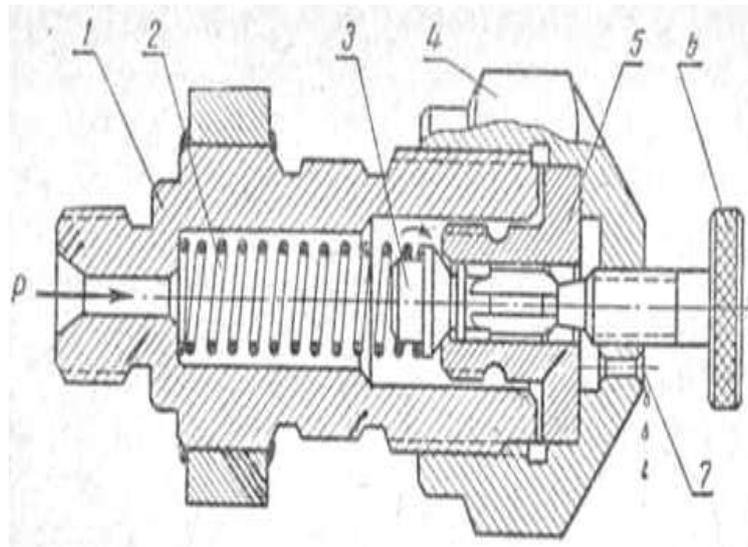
приспособление к прибору КП-1640А для проверки плотности прецизионной пары (обратный клапан- седло): 1- корпус; 2- пружина клапана; 3- клапан; 4- стяжная муфта; 5- седло; 6- винт; 7- сливное отверстие
